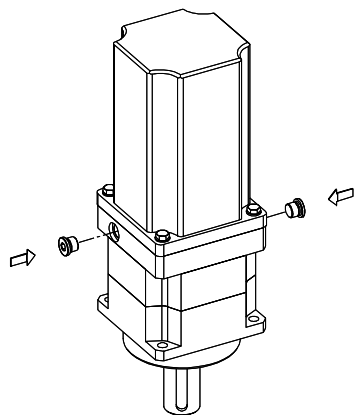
Verschließen der Montageöffnungen mit Verschlusschrauben
